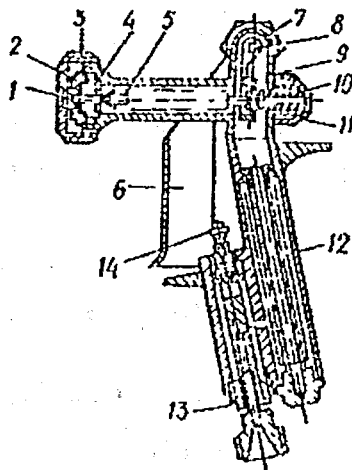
Пістолет-розпилювач до установки УБГХ-1М: 1 - насадка; 2 - фіксувальна втулка; 3, 11 - накидні гайки; 4 - сидло клапана; 5 - голчастий клапан; 6 - курок; 7 - кронштейн; 8 - вісь; 9 - важіль; 10 - підтискна пружина; 12 - корпус фільтра з сіткою; 13 - втулка з гайкою; 14 - запобіжник із пружиною
